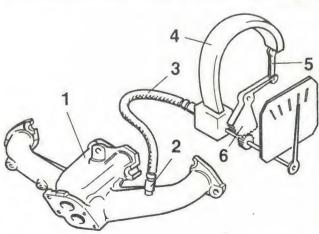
Схема соединения вакуумметра с впускным коллектором: 1 — впускной коллектор; 2 впускной коллектор; 2— штуцер; 3— соедини-тельный шланг; 4— упругая трубка в рабо-чем механизме вакуум-метра; 5— тяга; 6— зубчатый сектор испол-нительного механизма.
